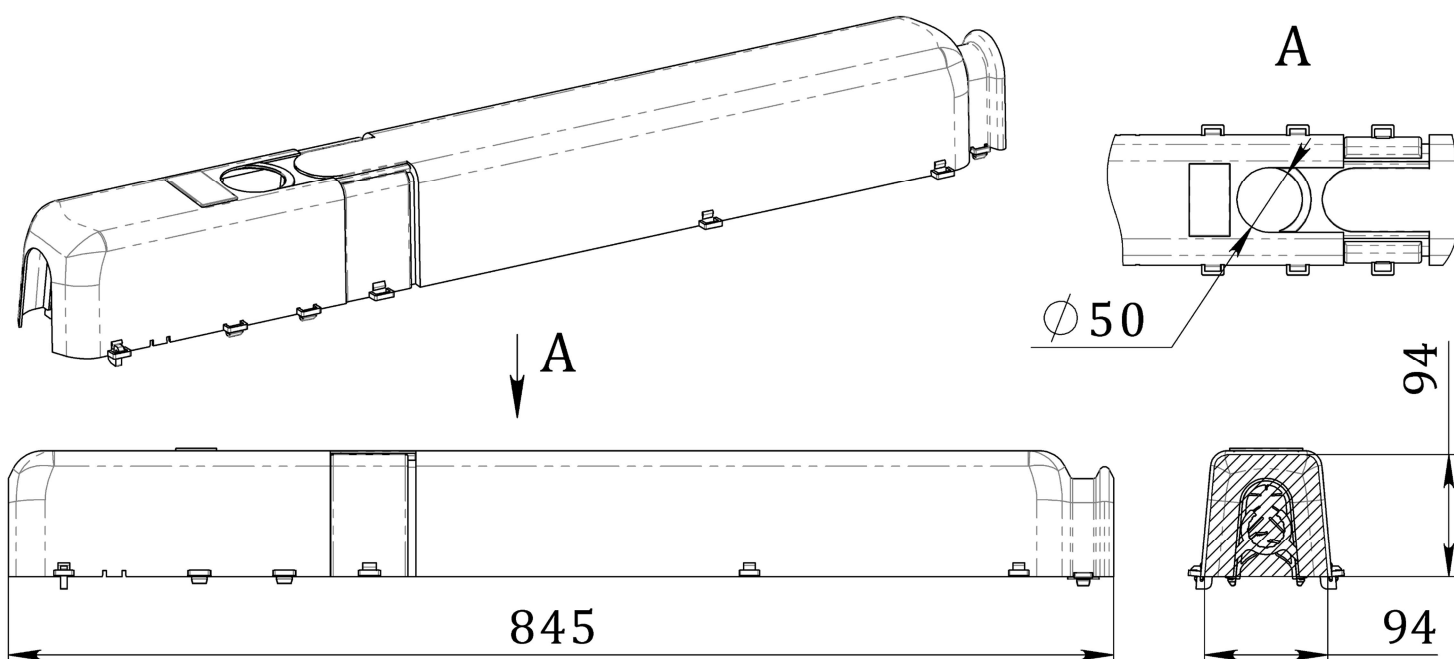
Общий вид и основные размеры ПЗУ-ВРА (кожух с отверстием)
